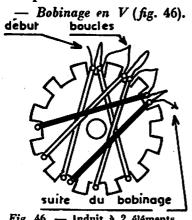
Induit à 2 éléments. Bobinage en V.
